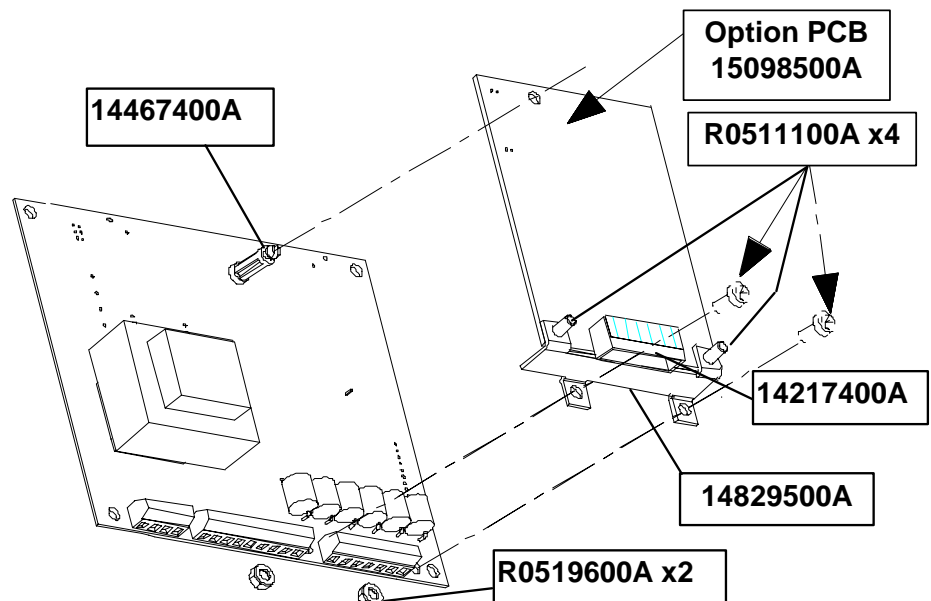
Instalación de la PCB Allen-Bradley en el gabinete de montaje en panel
